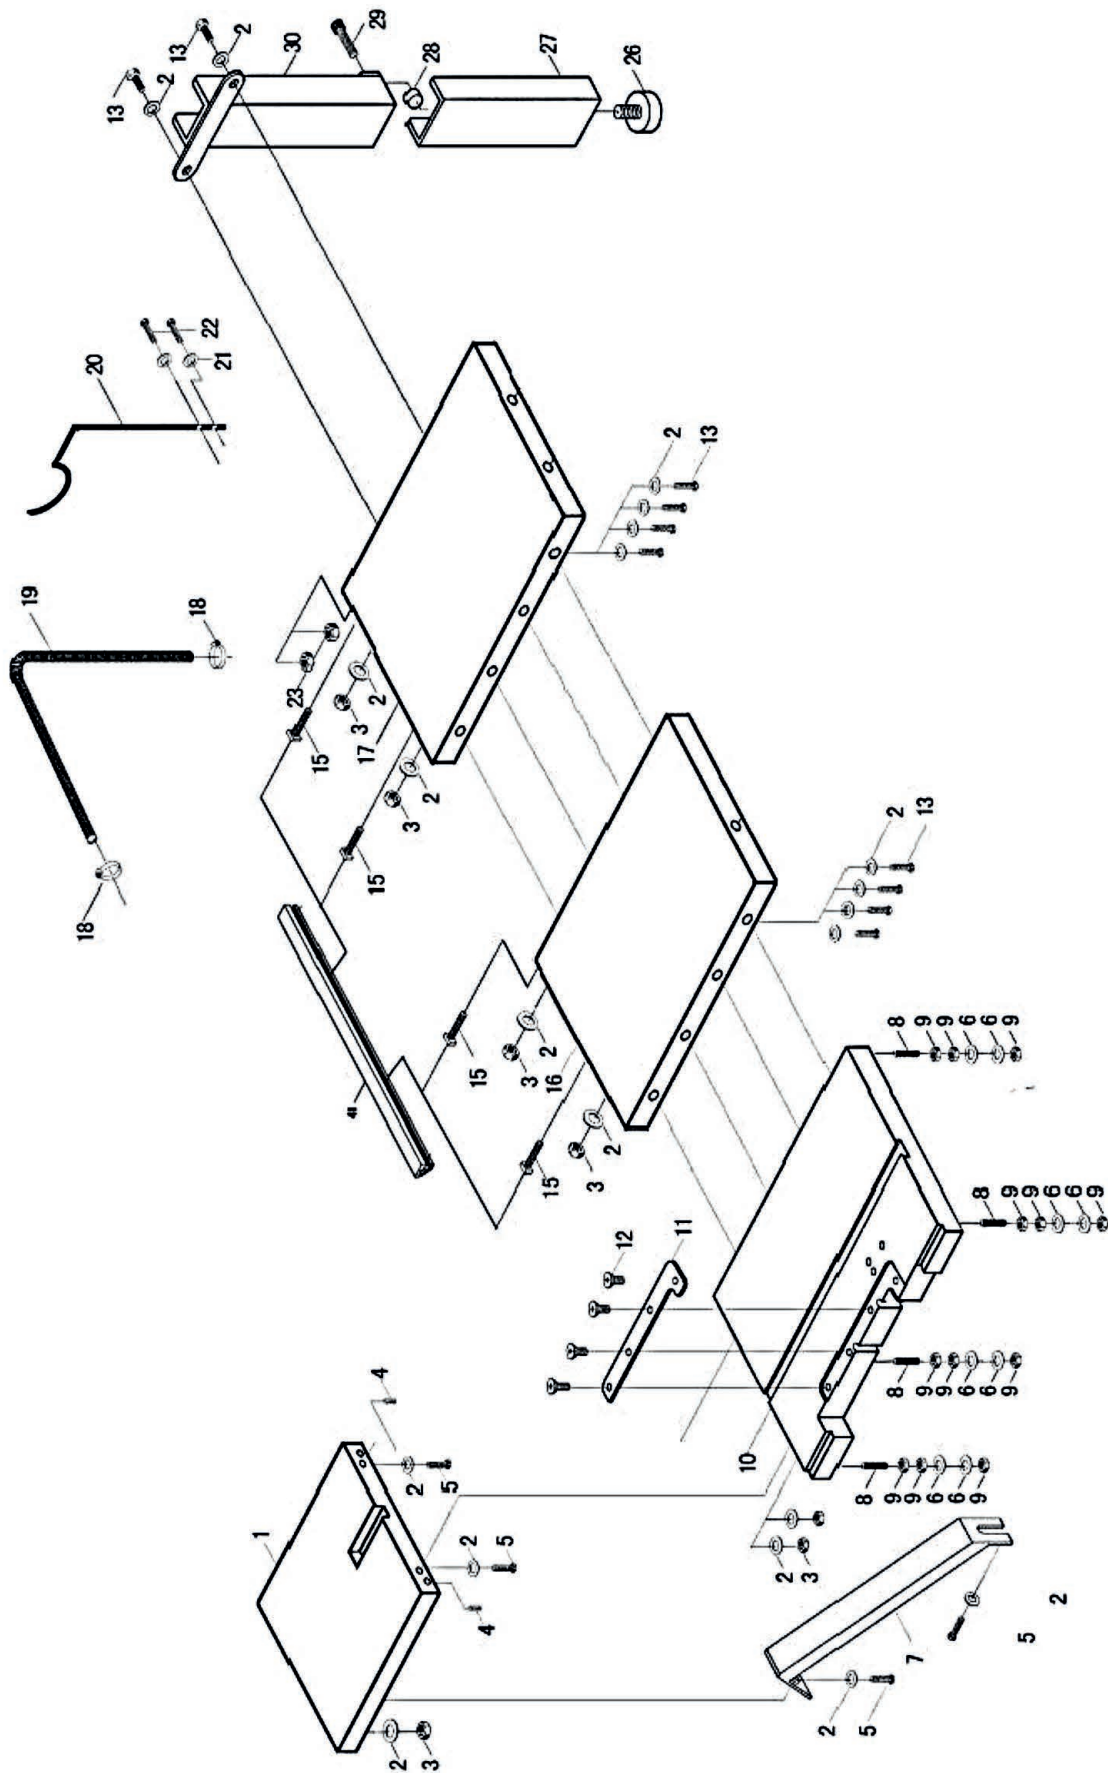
Dessin des pièces détachées 7 - Scie à format FKS 315-2000 E
